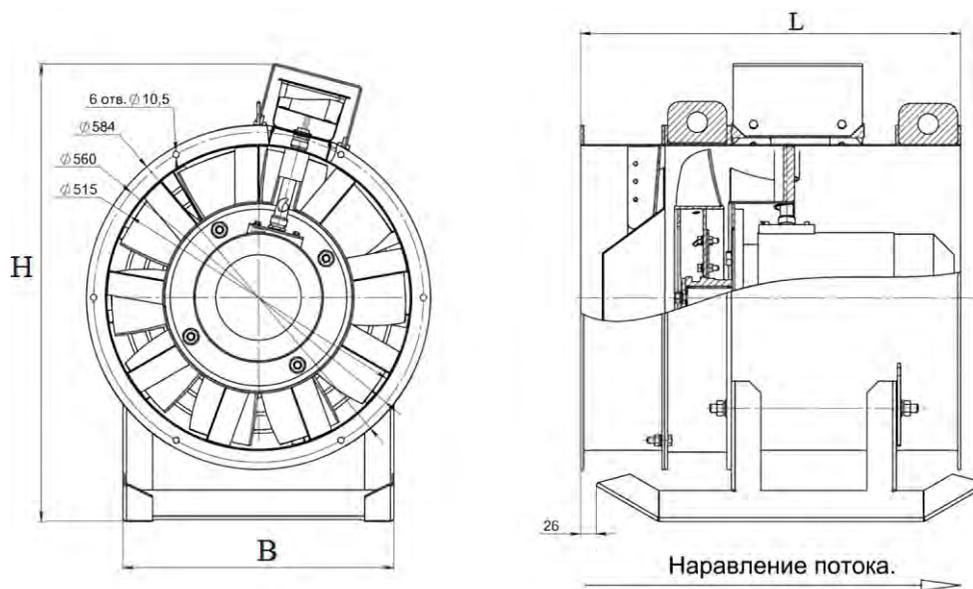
Габаритные и присоединительные размеры вентилятора ВОЭ.
